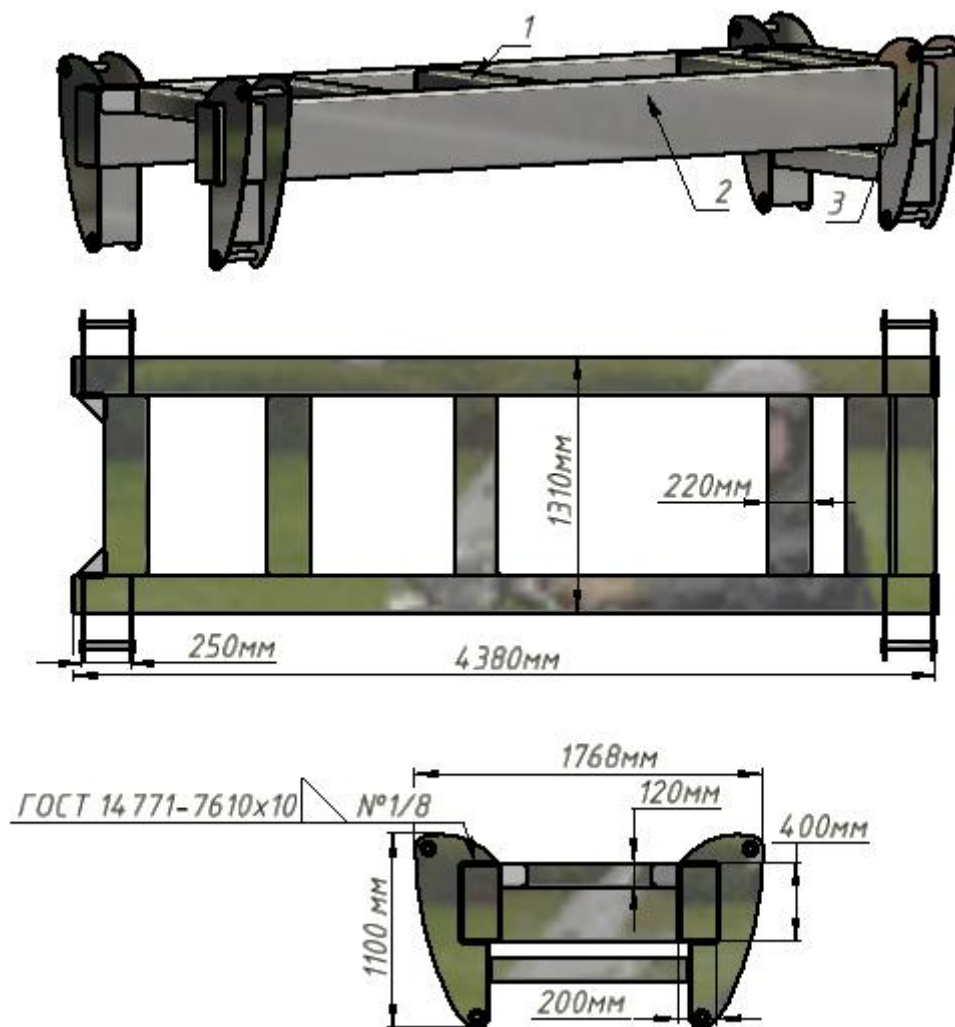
Загальний вигляд рами ескаватора ЭОВ – 4122
